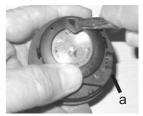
FIXIERUNG DES HAL-TERINGS
